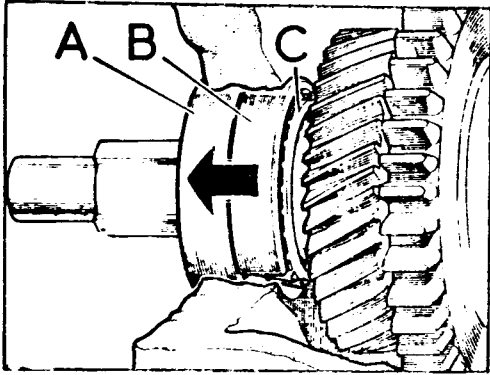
Desmontaje de la pista exterior del cojinete
